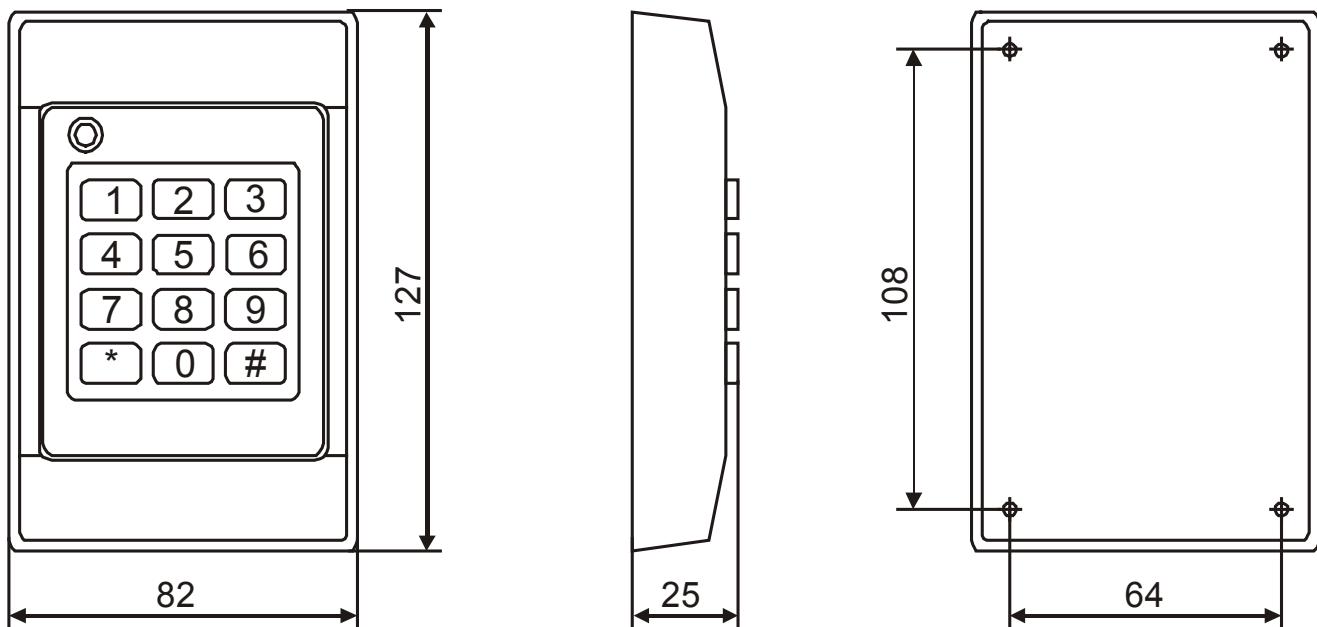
Внешний вид и габаритные размеры УСК-02К
